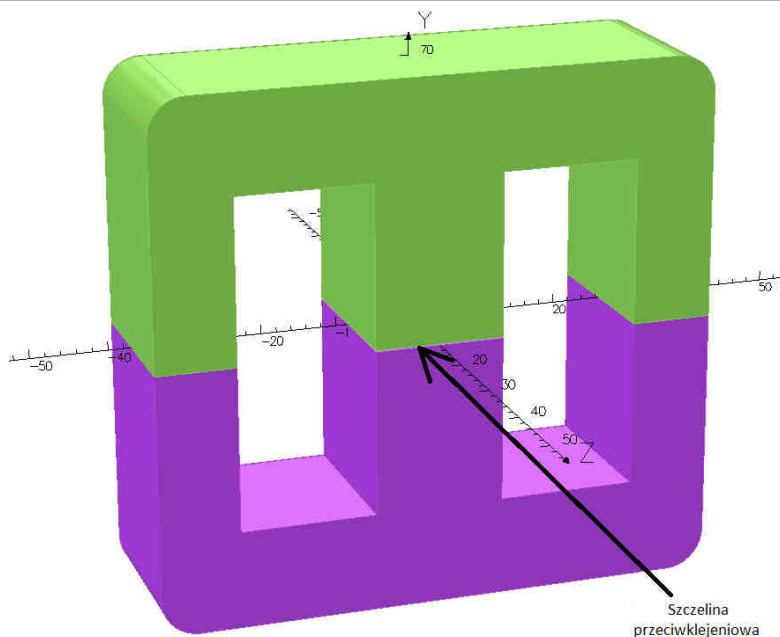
Zaokrąglone narożniki zwory i rdzenia
